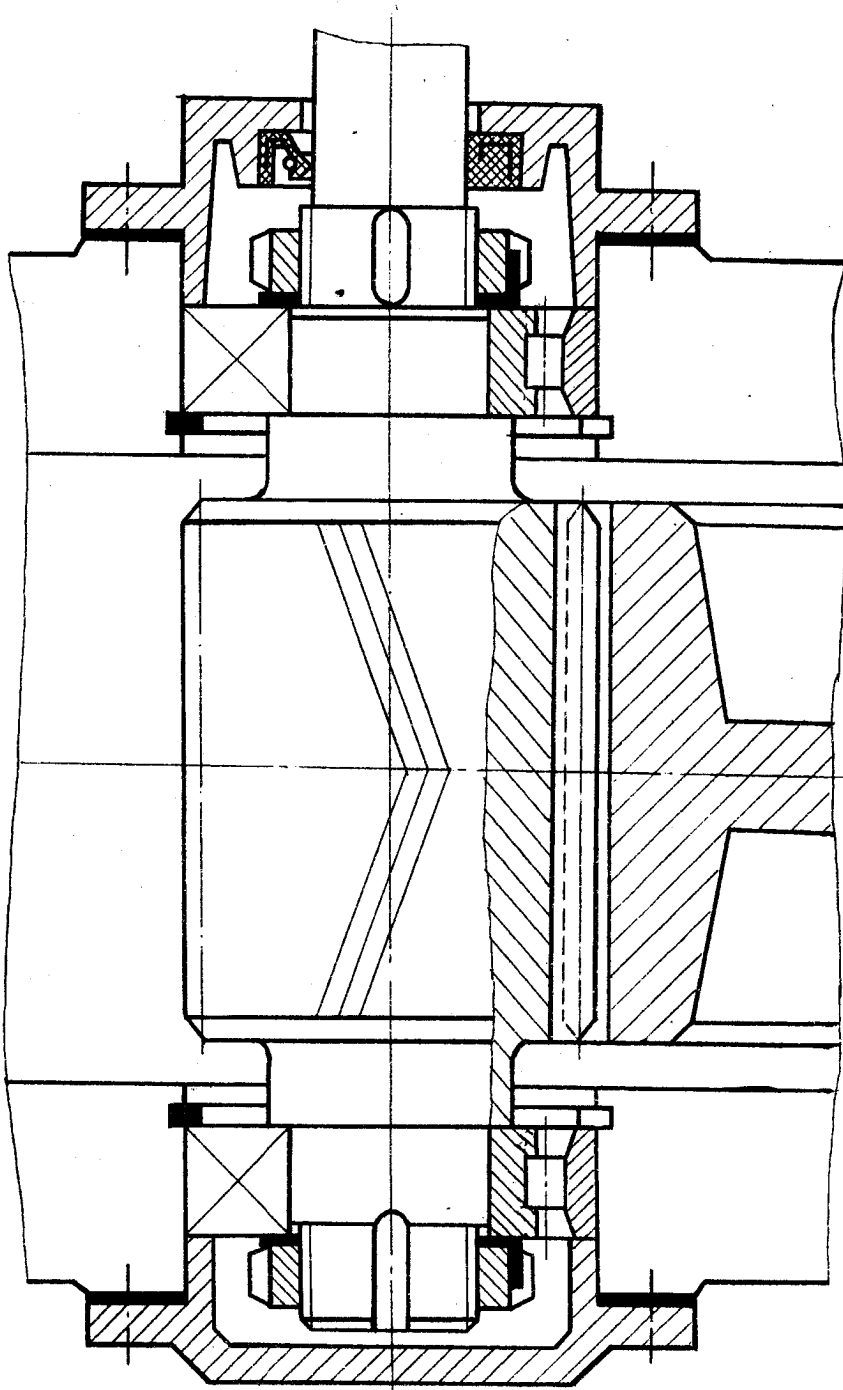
Підшипниковий вузол з двома тавуючими опорами
